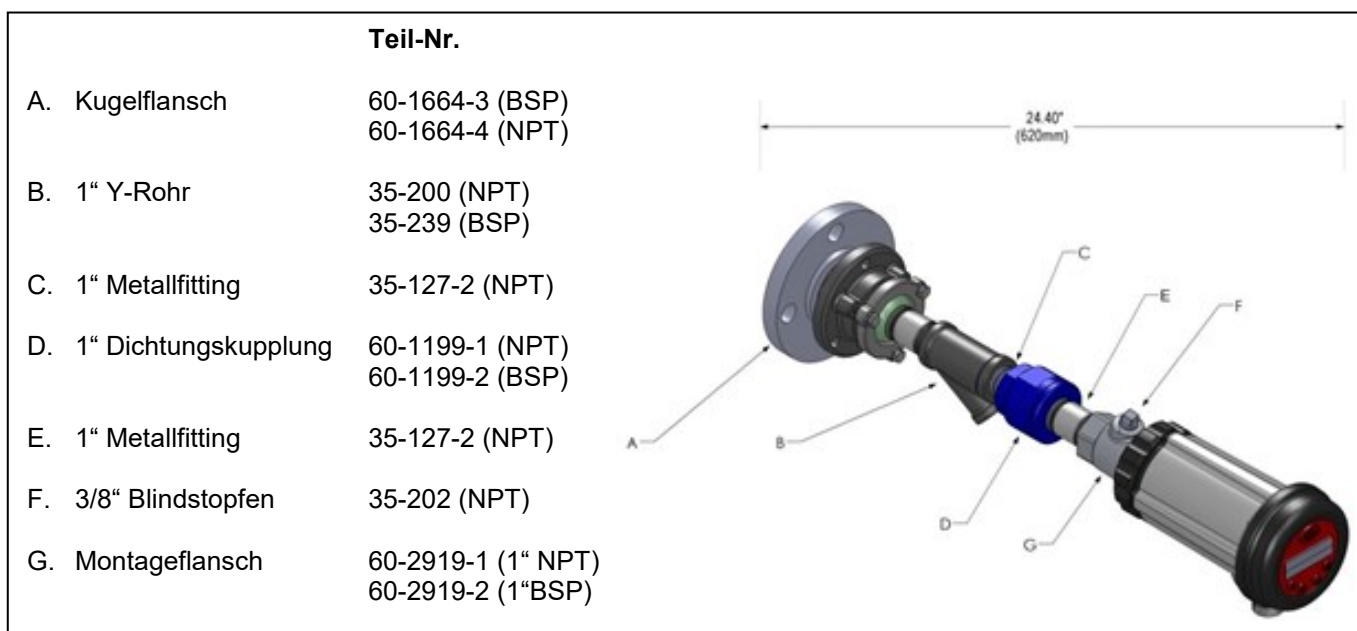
Flammenwächter mit Kugelflansch, Y-Stück, Metallfitting, Blindstopfen, Montageflansch
